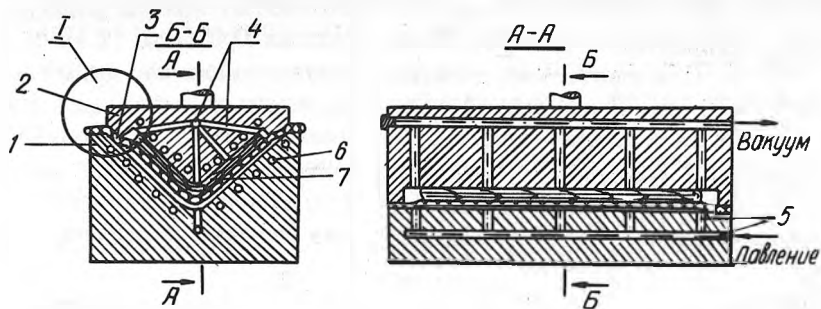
Вакуумная пресс-форма с жестким бортом из металла: 1—матрица; 2—пуансон; 3—эластичная диафрагма; 4—система отверстий для удаления воздуха из вакуум-камеры; 5—система отверстий, сообщающихся с атмосферой; 6—гэны; 7—пакет.
